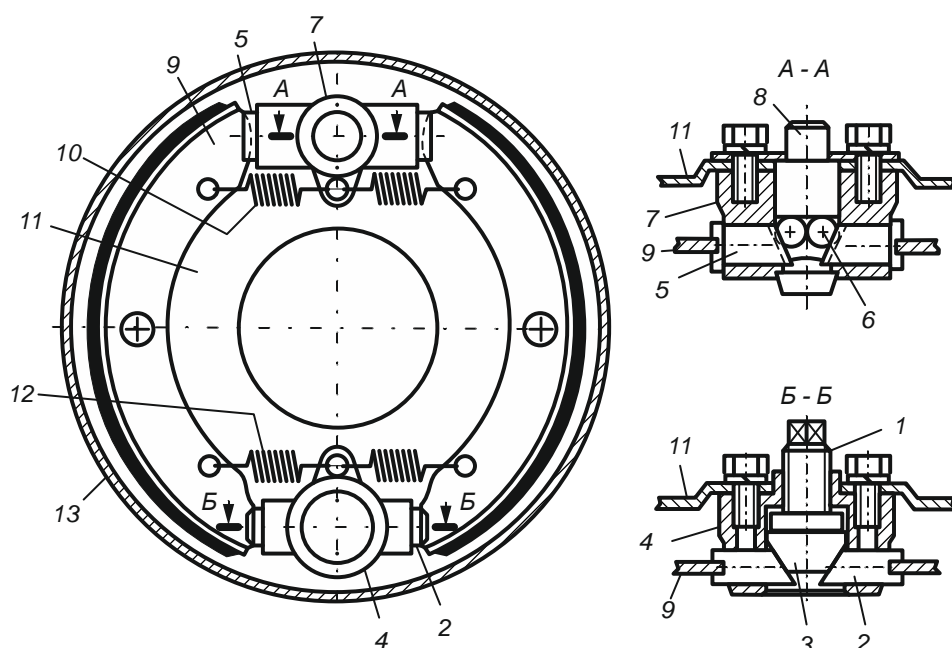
Схема центрального барабанного тормоза с двумя внутренними колодками:
